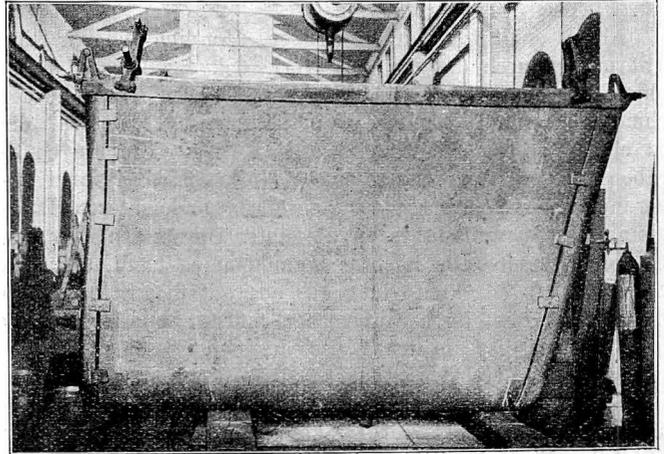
Feuerbüchsenrohr- und Rückwand zum Schweißen zusammengespant.
